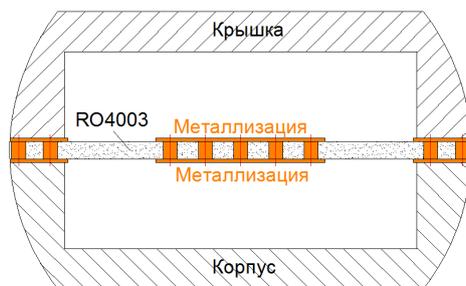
Разрез конструкции линии передачи мощного СВЧ сигнала
